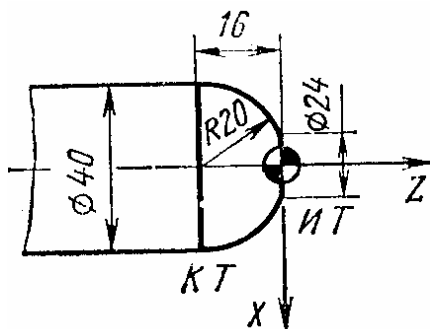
Эскиз заготовки (к заданию 16.9)
